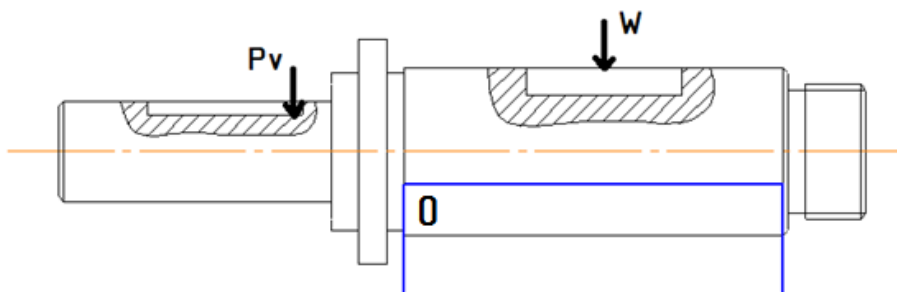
Схема для определения силы закрепления W . Вид сбоку.
